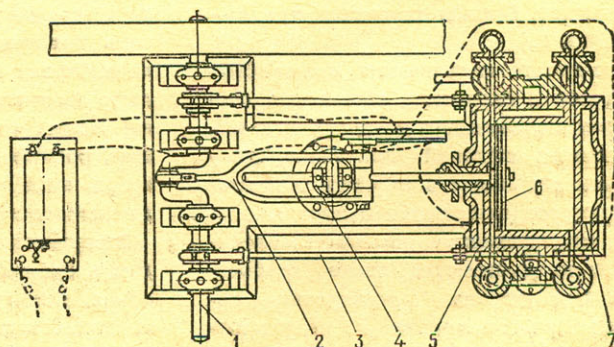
Двигатель Ленуара: 1 — коленвал, 2 — шатун, 3 — шток золотника, 4 — направляющая штока поршня, 5 — золотник, 6 — поршень, 7 — свеча.
